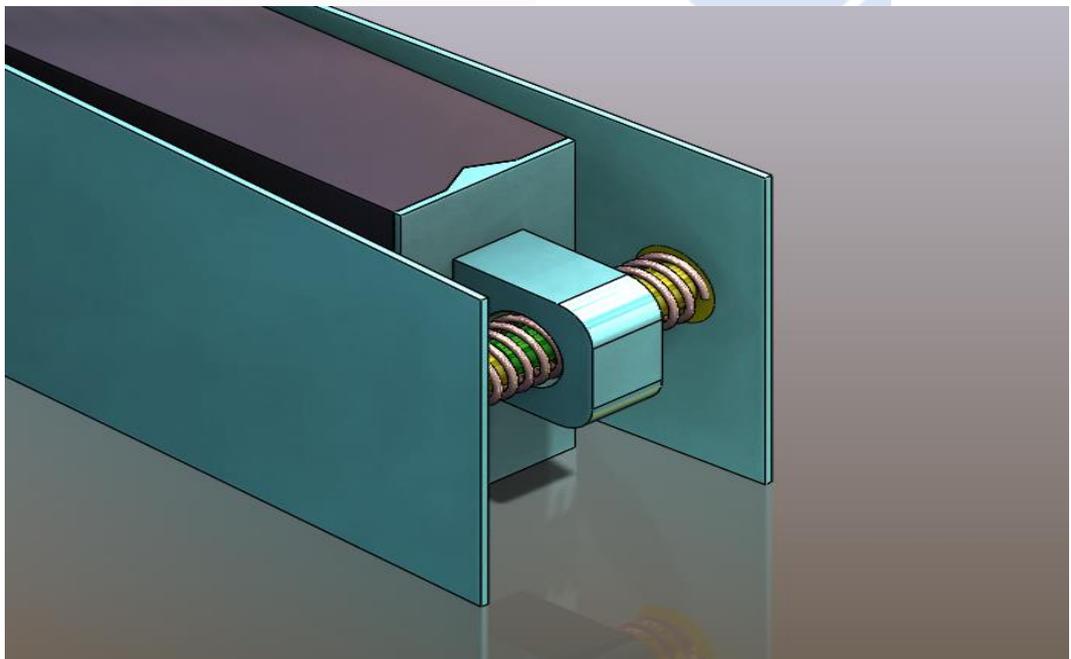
Adonan Balok Plastik yang Telah Mengeras
